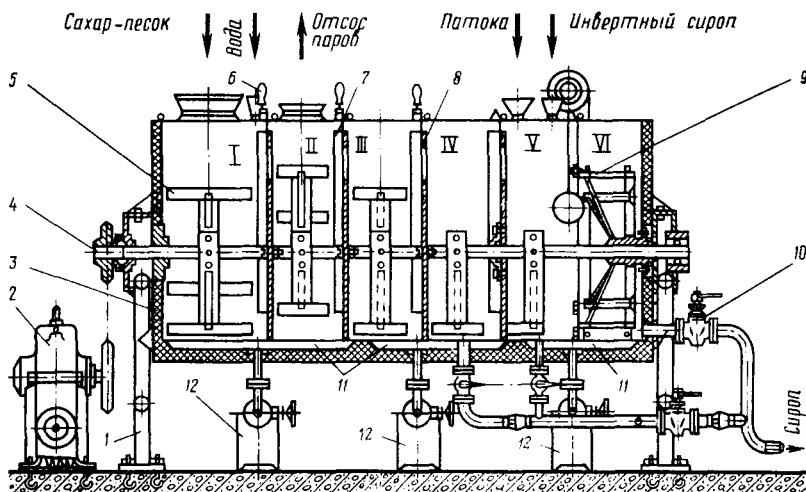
Шестисекционный растворитель для приготовления сахарного сиропа
